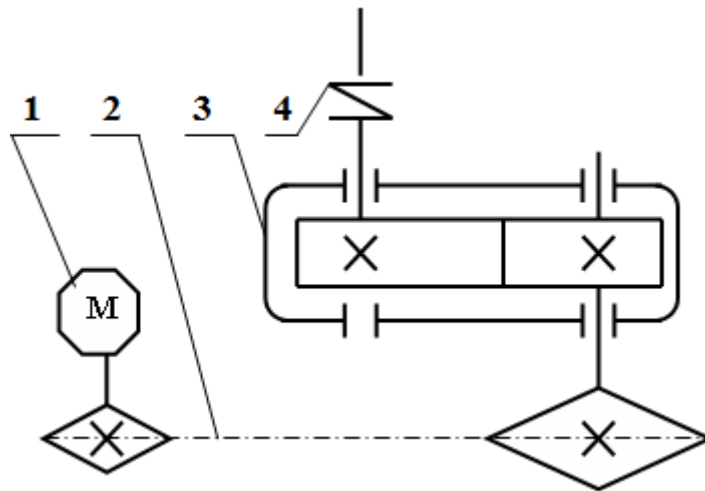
Привод люлечного конвеєра: 1 – електричний двигун, 2 – ланцюгова передача, 3 – одноступінчатий циліндричний прямозубий редуктор, 4 – муфта типу МПВП.
